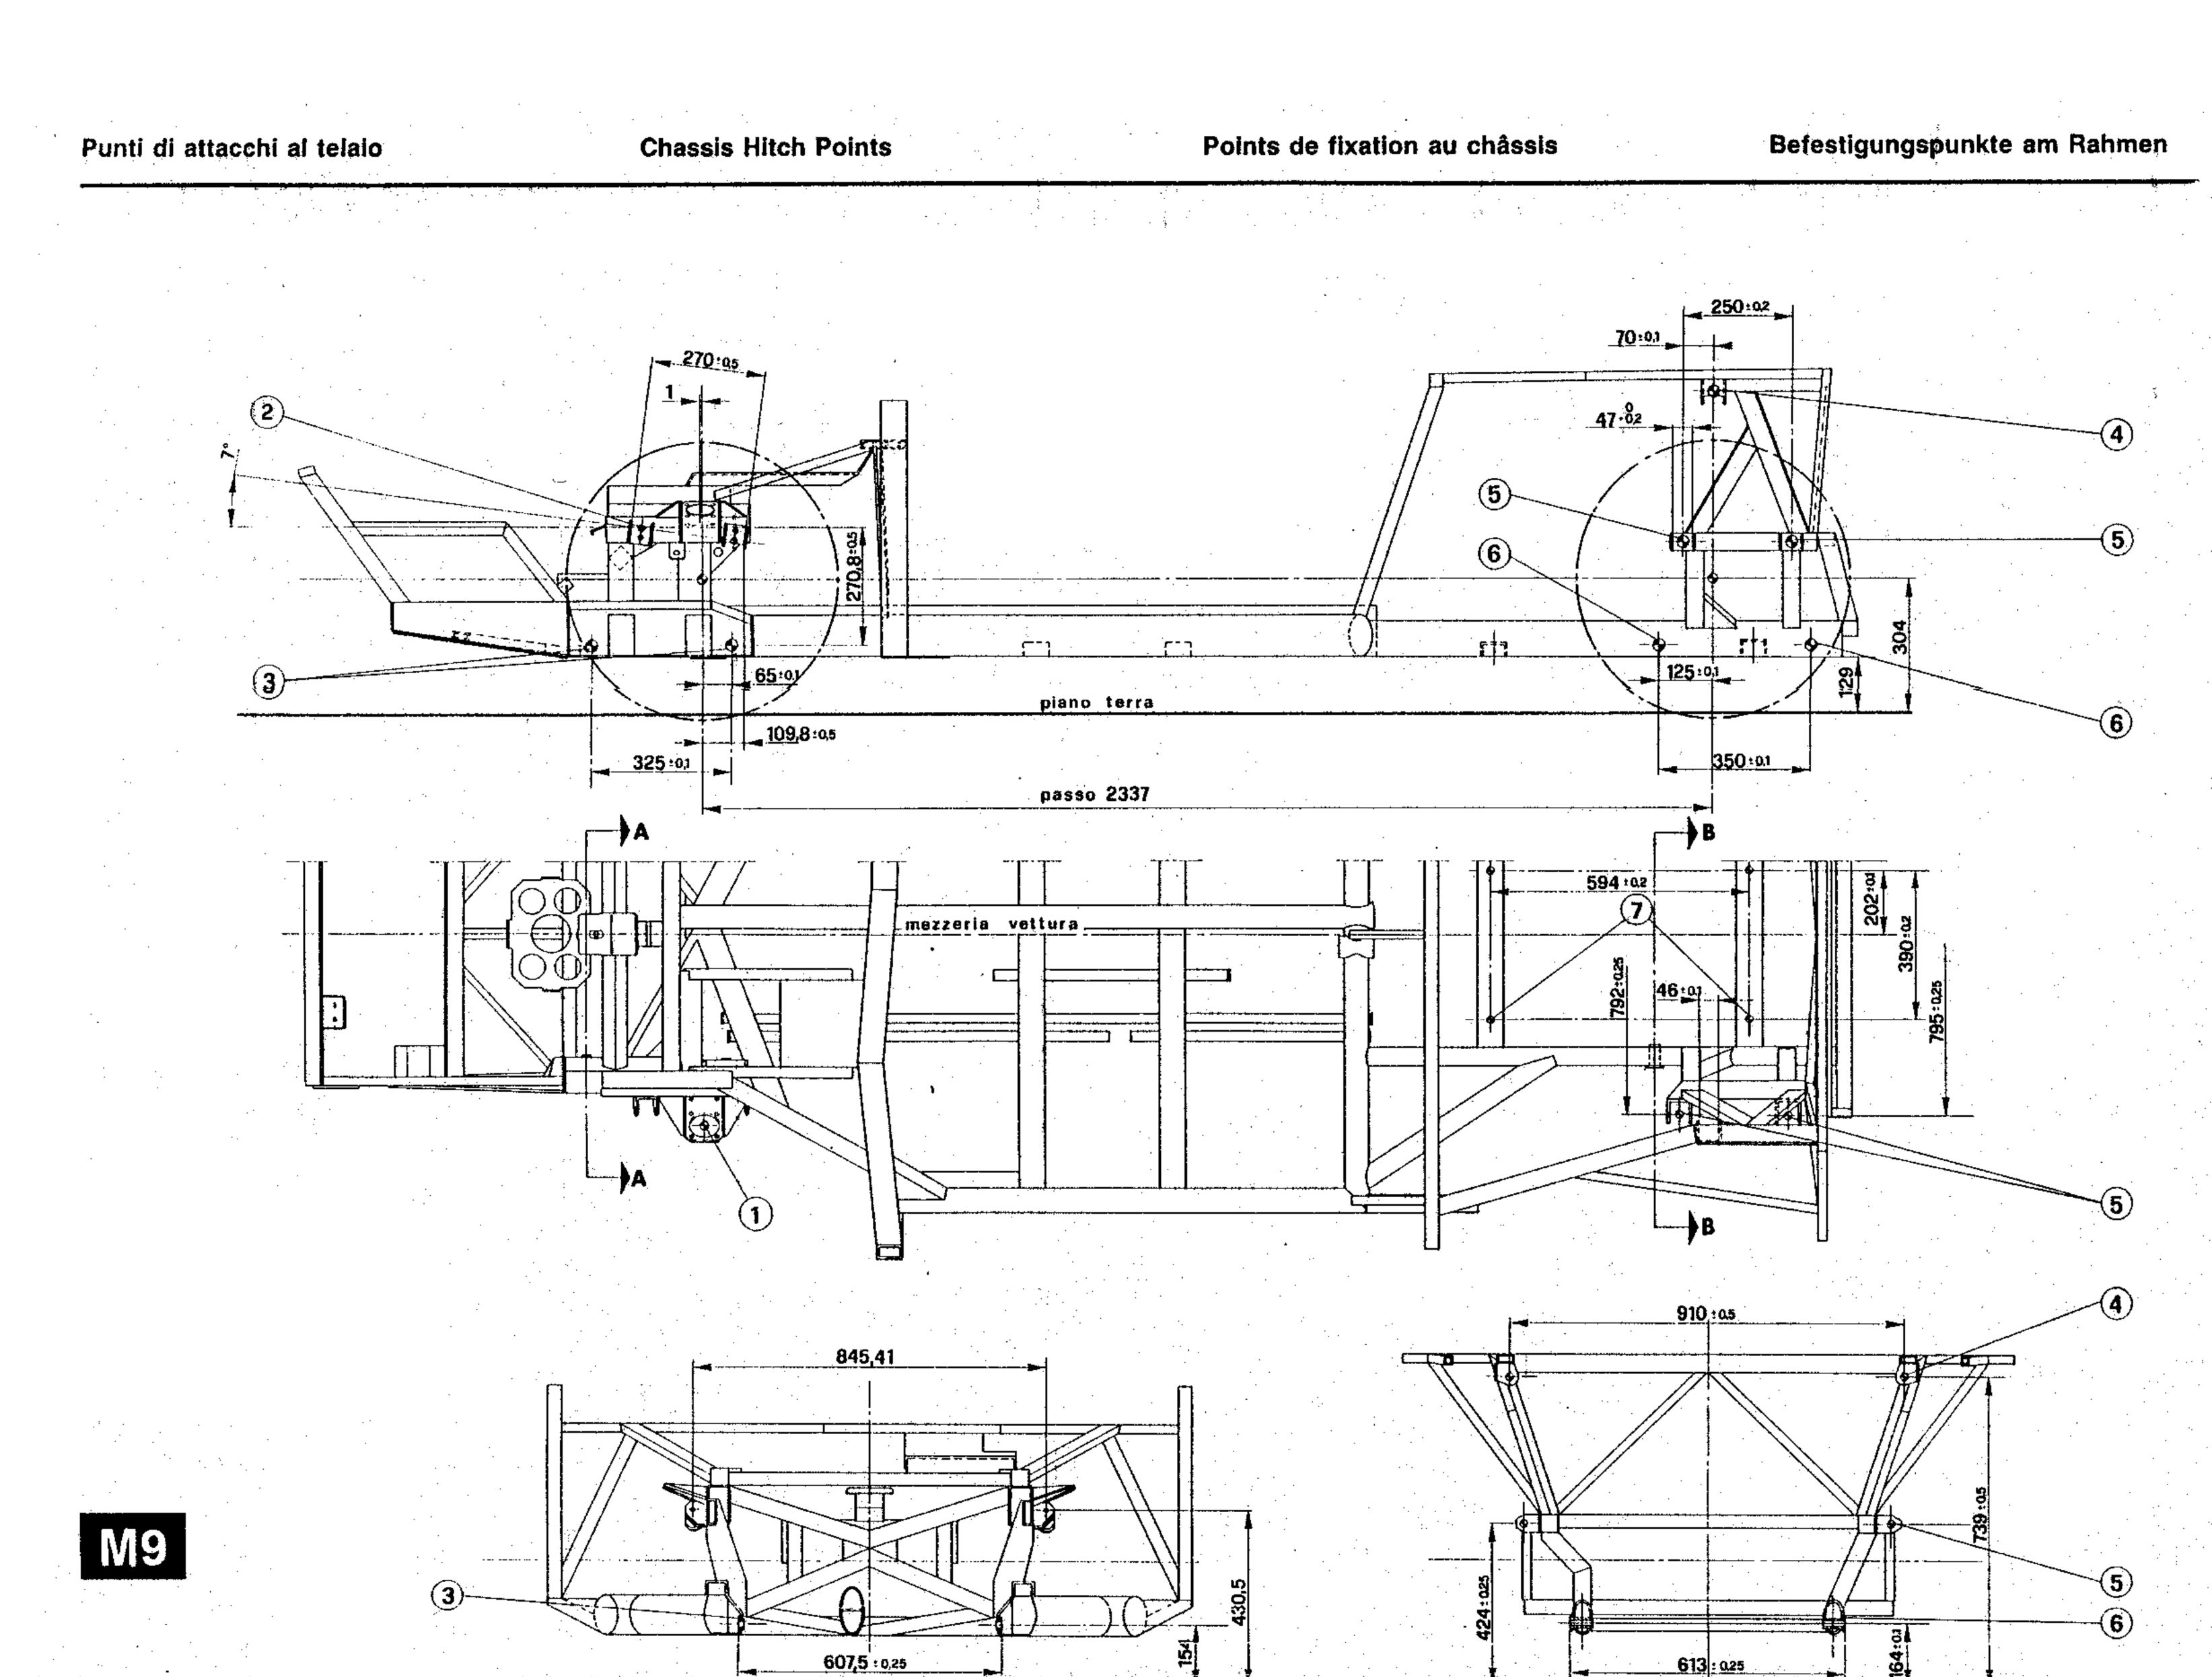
= Punti di attacco al telaio 328 (Dalla vettura N. 76626)
